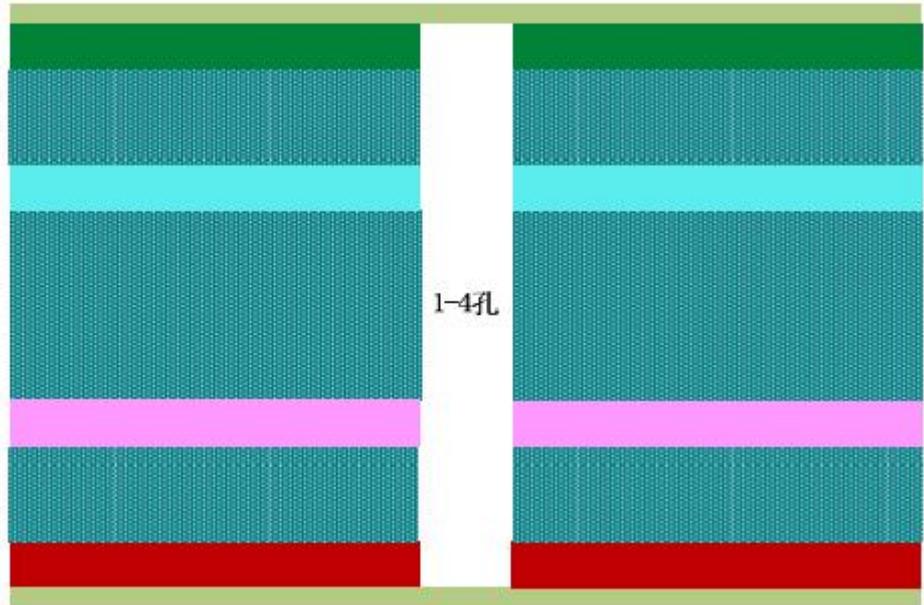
1.6mm 厚通孔 PCB 板叠层示意图
